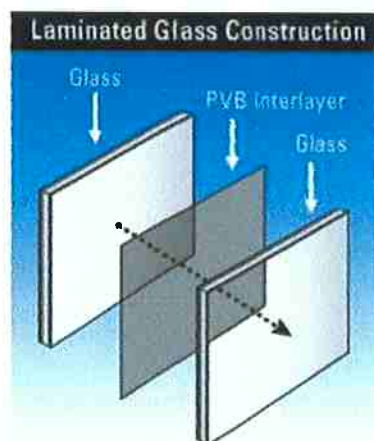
Ilustração da fabricação do vidro laminado [26].
